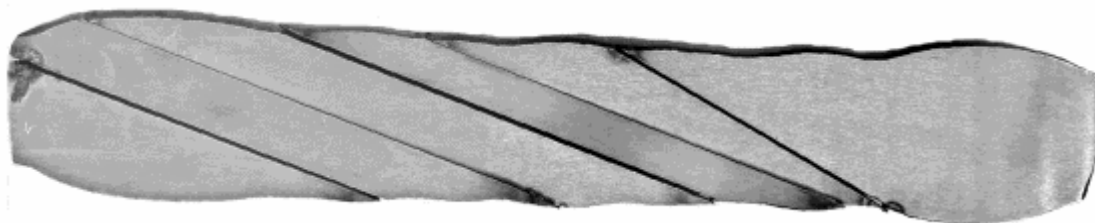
Внешний вид образцов стали марки Р6М5 после газолазерной резки
